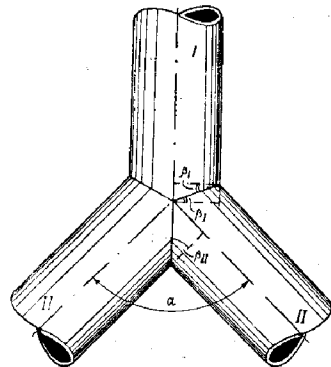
Сварной тройник разветвленный (штан).
